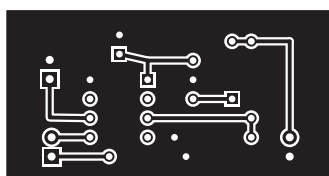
Die Schaltung wurde auf einer Universalplatine mit ausgedrucktem Layout aufgebaut. Fotos: DL1MK
